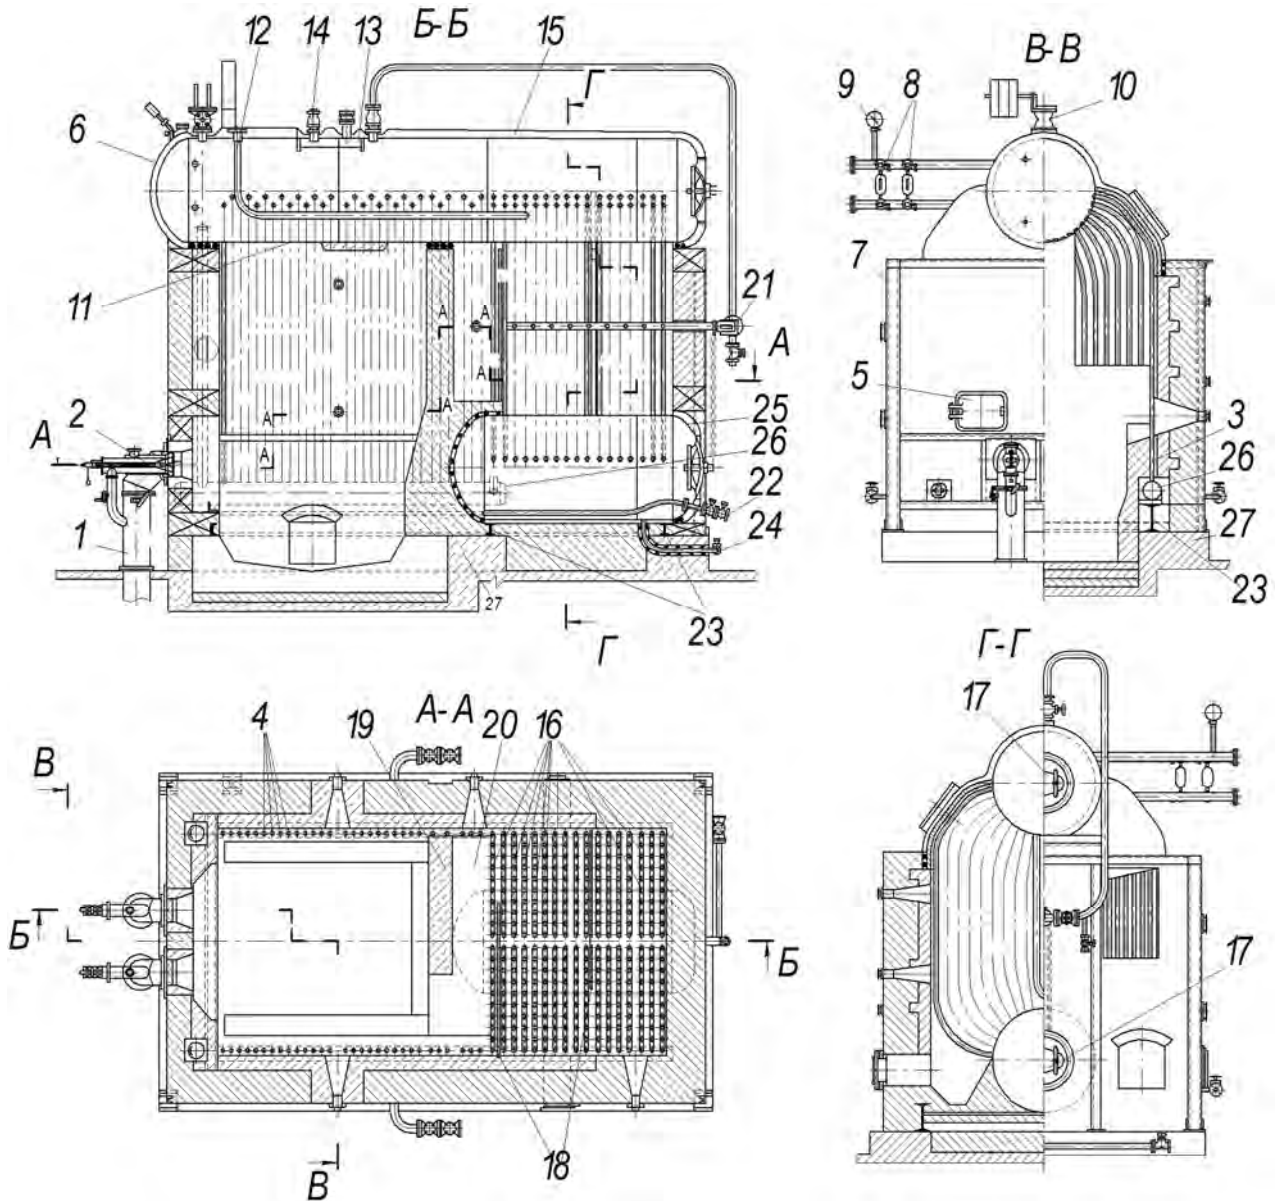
Паровой котел ДКВР-4/13: 1 – воздуховод; 2 – горелка; 3 – труба опускная; 4 – трубы экранные; 5 – дверца топки; 6 – верхний барабан котла; 7 – каркас обмуровки; 8 – водоуказательная колонка; 9 – манометр; 10 – предохранительный клапан; 11 – легкоплавкая пробка; 12 – подвод питательной воды; 13 – сепарационное устройство; 14 – главная паровая задвижка; 15 – теплоизоляция барабана котла; 16 – трубы конвективного блока; 17 – люк-лаз барабана; 18 – перегородка; 19 – кирпичная перегородка; 20 – камера догорания; 21 – обдувочный аппарат; 22 – труба периодической продувки; 23 – опоры котла; 24 – дренажная труба; 25 – нижний барабан котла; 26 – коллектор экрана; 27 – фундамент котла
